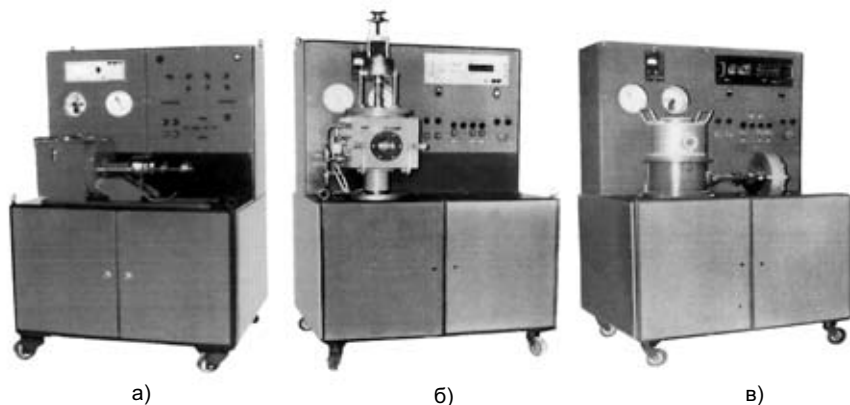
Сварочная установка "Стык-3": а — основной вариант установки; б — установка с вертикальным расположением осей свариваемых заготовок; в — то же, с пневмодиафрагменным механизмом осадки
